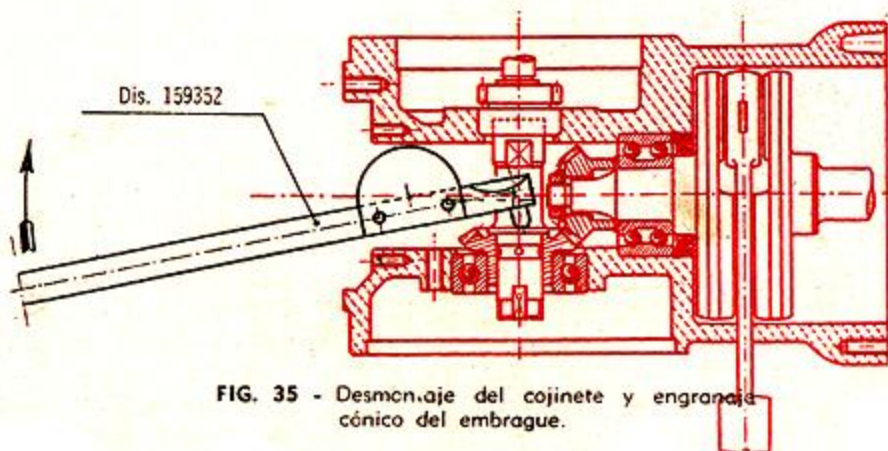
Desmontaje del cojinete y engranaje cónico del embrague.
